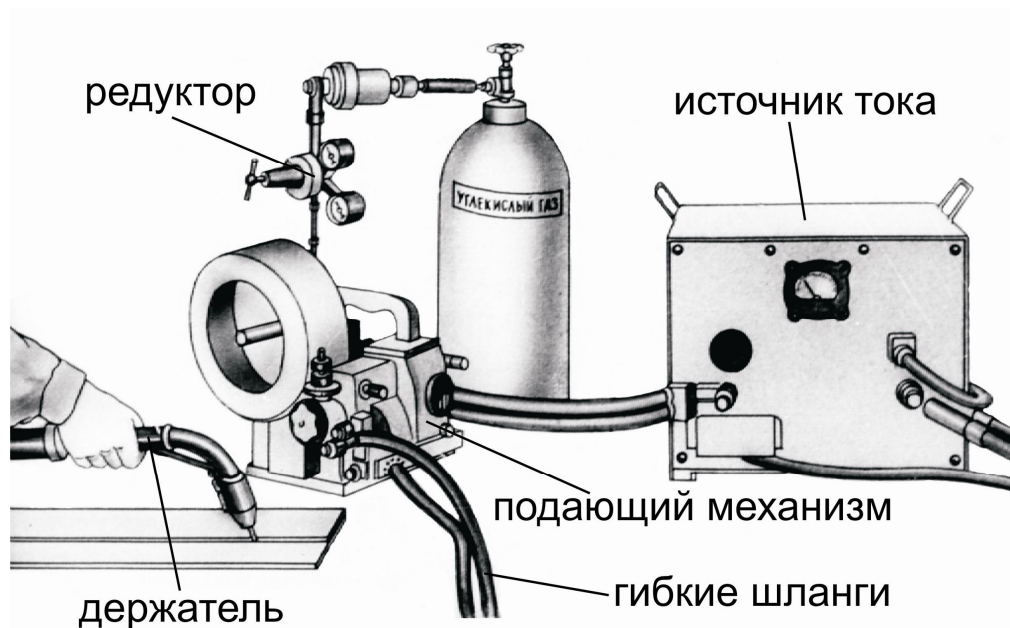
Общий вид установки для механизированной сварки в защитных газах
